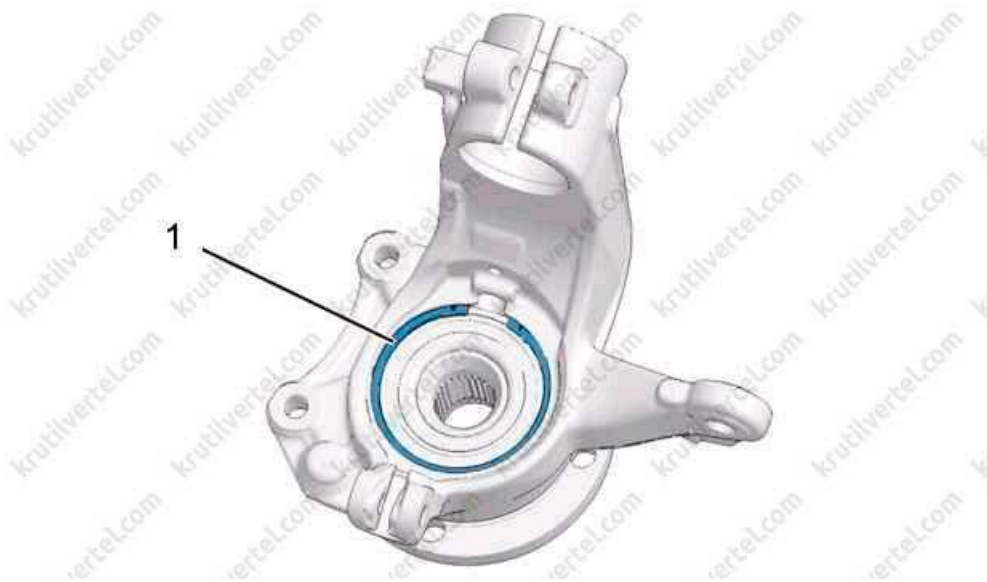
Демонтаж пружинного стопорного кільця:
